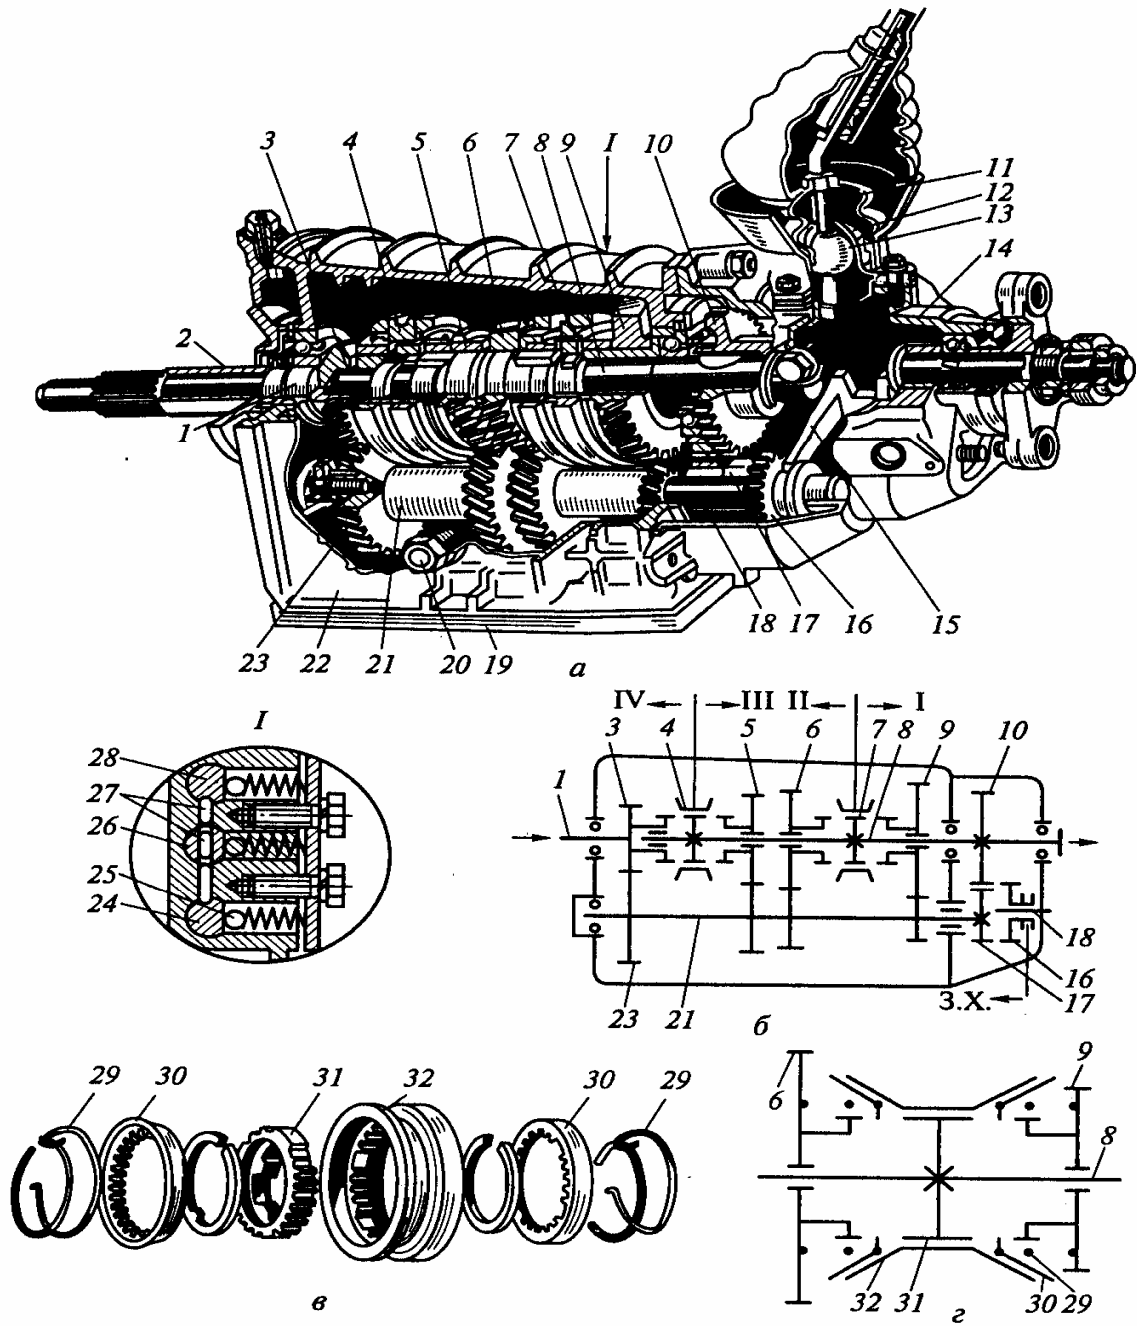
Коробка передач легковых автомобилей ВАЗ:
